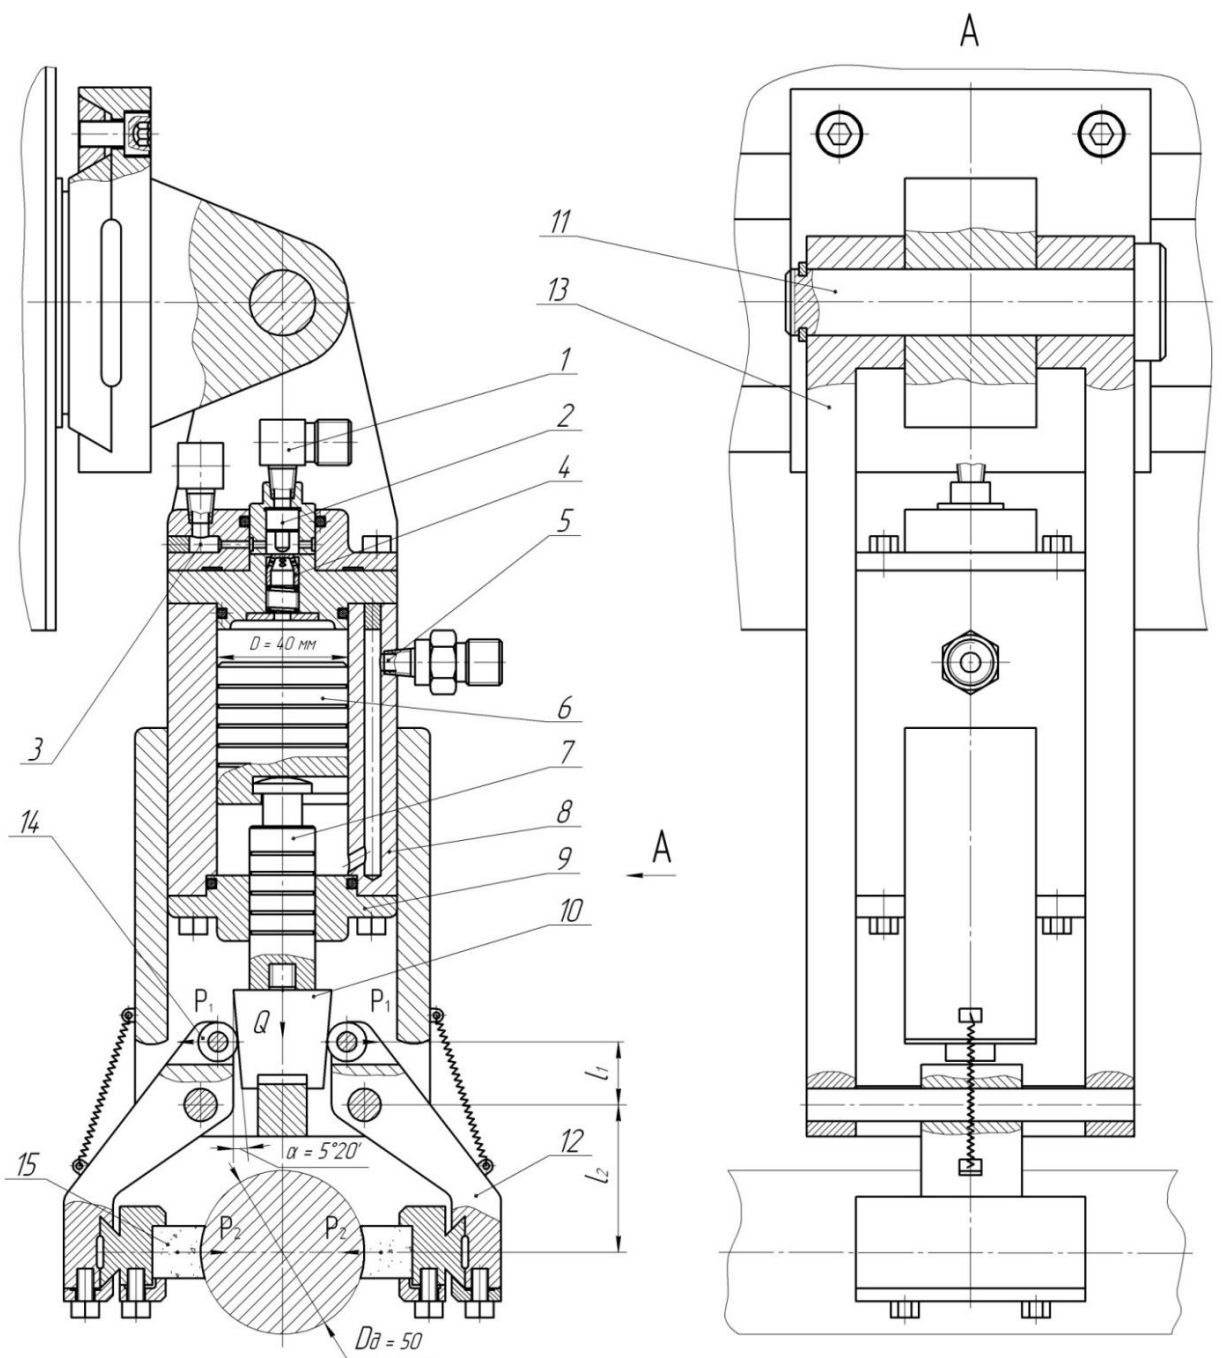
Інструментальна головка для зовнішнього хонінгування
